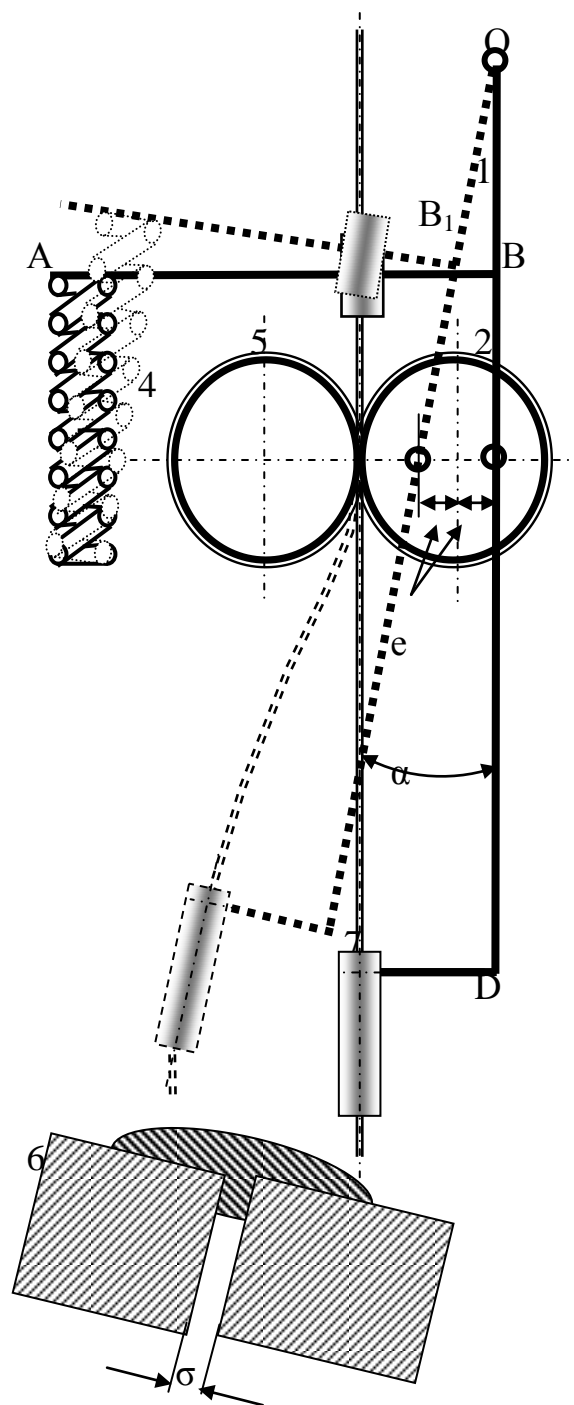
Схема колебателя сварочной горелки: 1 – рычаг; 2 – прижимной ролик; 3 – сварочная горелка; 4 – пружина сжатия; 5 – подающий ролик; 6 – элементы конструкции (условно); 7 – электродная проволока
